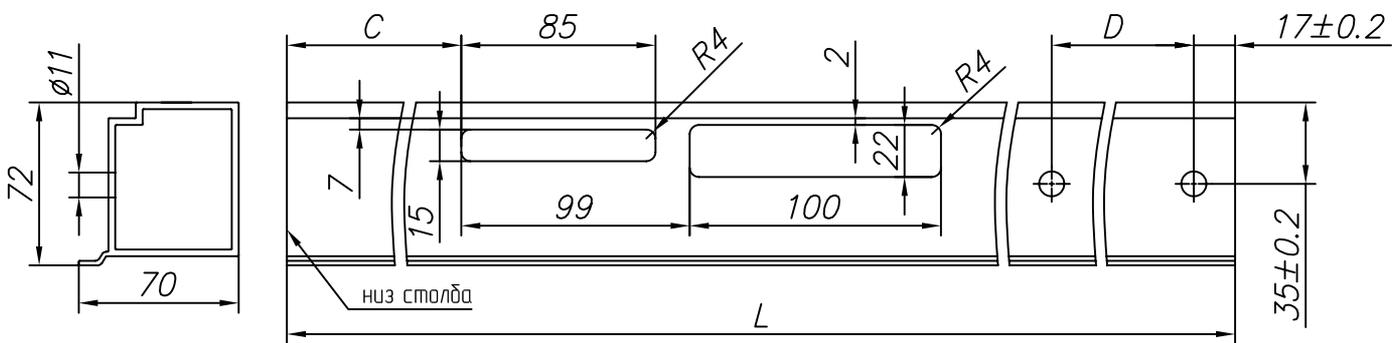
Изготовление столба притвора с пазом для автоматической защелки для калитки с правым открыванием (защелка 118WE)
